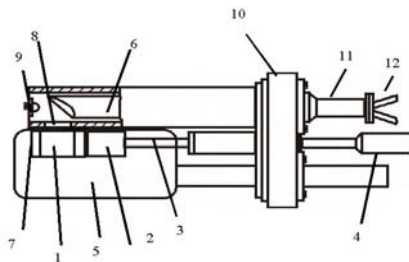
Рентгеновская трубка с приставкой для охлаждения.
